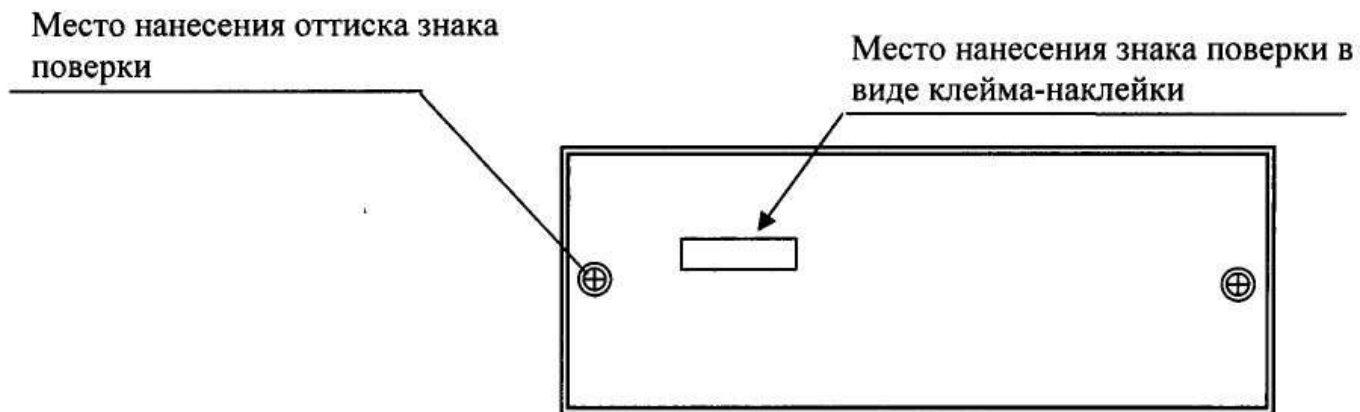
Место нанесения оттиска знака поверки и знака поверки в виде клейма-наклейки (вид генератора сзади)
